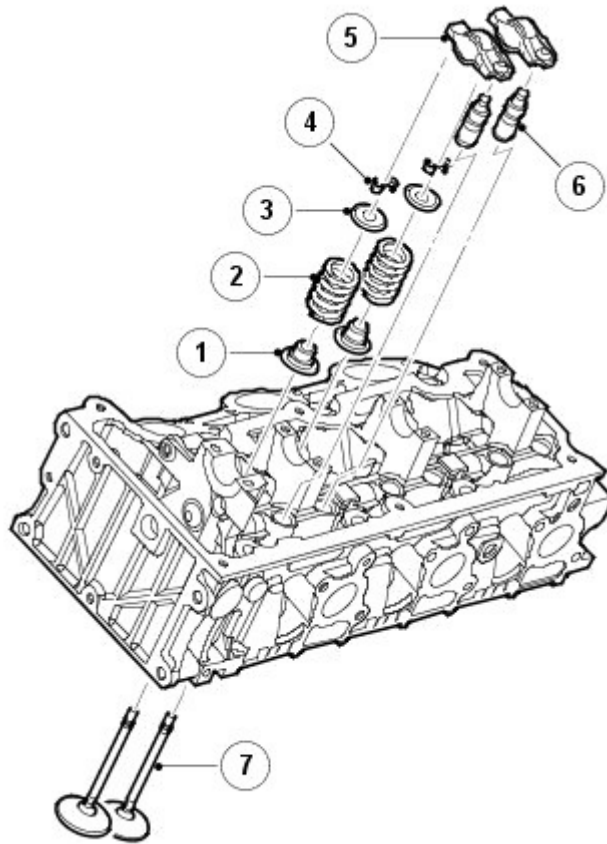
Клапаны и гидравлические регуляторы зазора бензинового двигателя 4.0L V6
